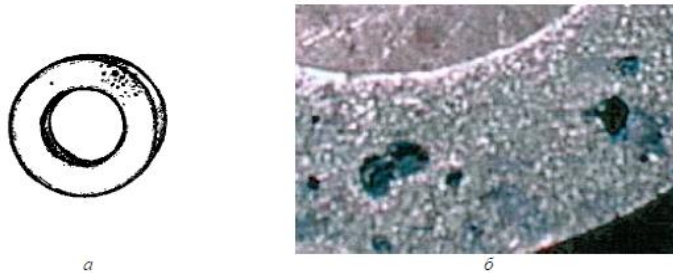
Дефект – шлаковая раковина: а – схема; б – дефектная отливка
